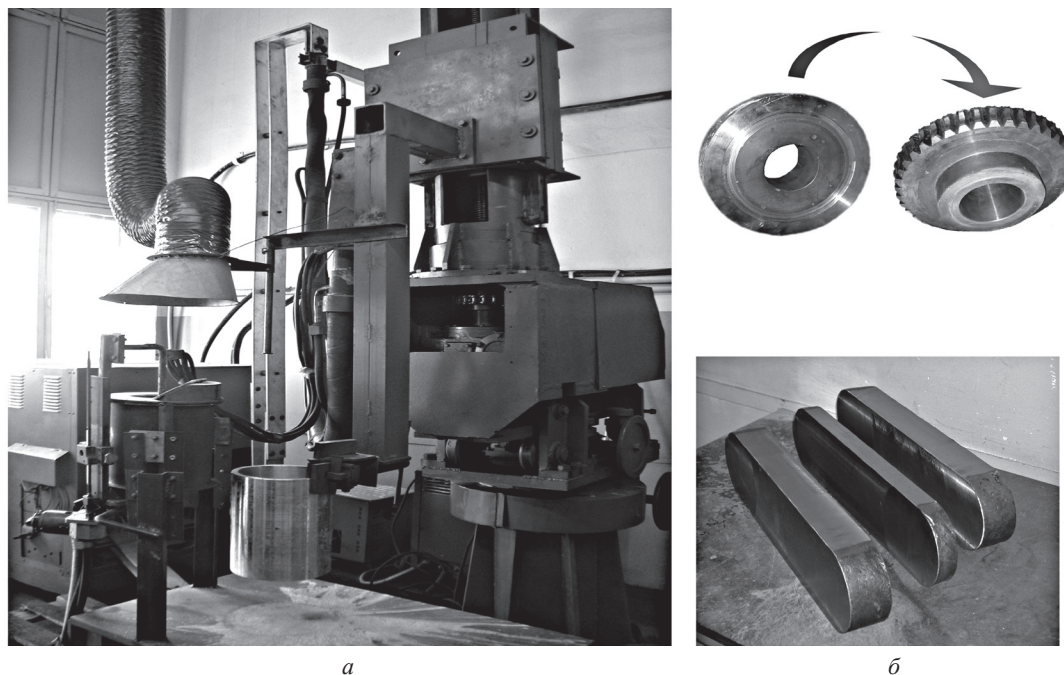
Технологическое оборудование изготовления заготовок деталей прокатного оборудования методом электрошлакового переплава (а) и вид стальных и биметаллических заготовок (б)
